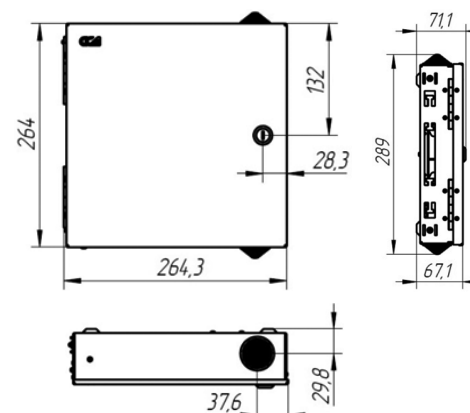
Габаритные размеры ШКОН-У 8/16
